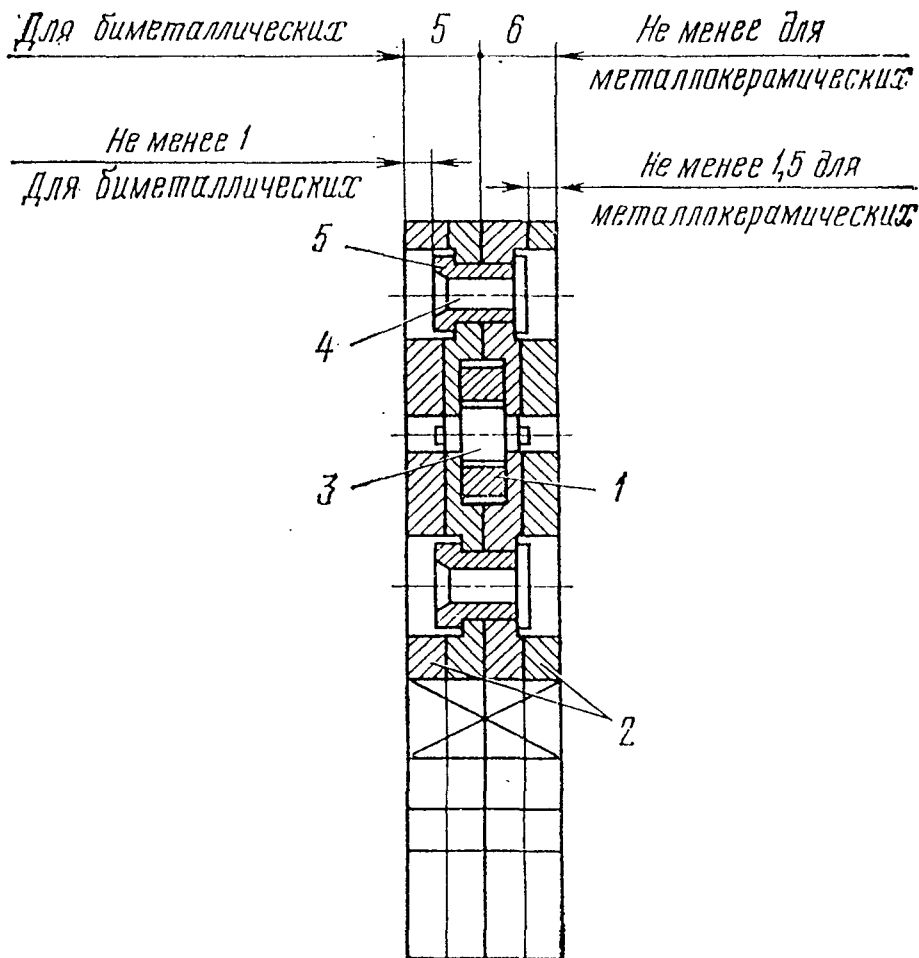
Крепление секторов биметаллических и металлокерамических дисков:
